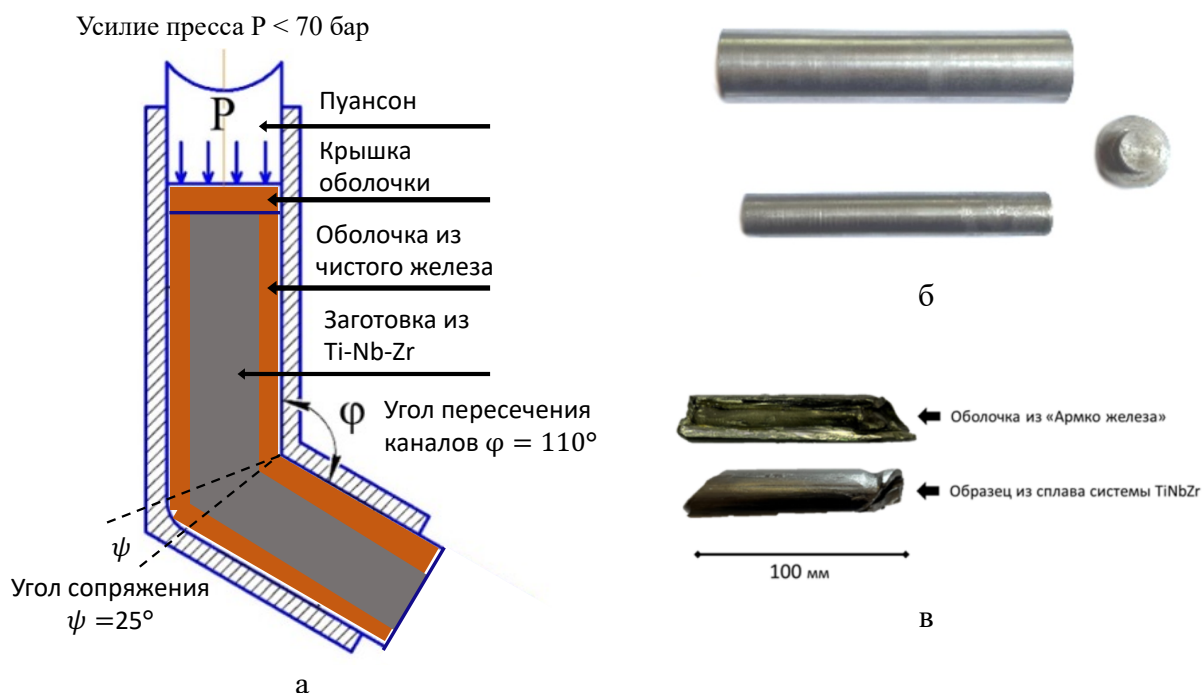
Равноканальное угловое прессование прутка из сплава Ti-39Nb-7Zr: схема оснастки для проведения РКУП (а), вид оболочки и заготовки перед (б) и после (в) деформации
